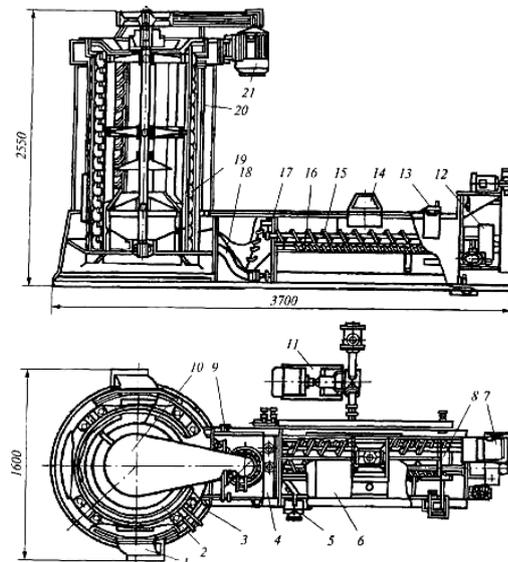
Мийна машина Ж9-БМБ: 1, 5 – випускні патрубки; 2 – віджимна колонка; 3 – зрошувач; 4 – зливальний пристрій; 6 – ванна; 7 – електродвигун; 8 – воронка; 9 – патрубок; 10 – захисне огороження; 11 – насосна установка; 12 – редуктор; 13 – каменевіддільник; 14 – приймальний пристрій; 15 – шнек для
